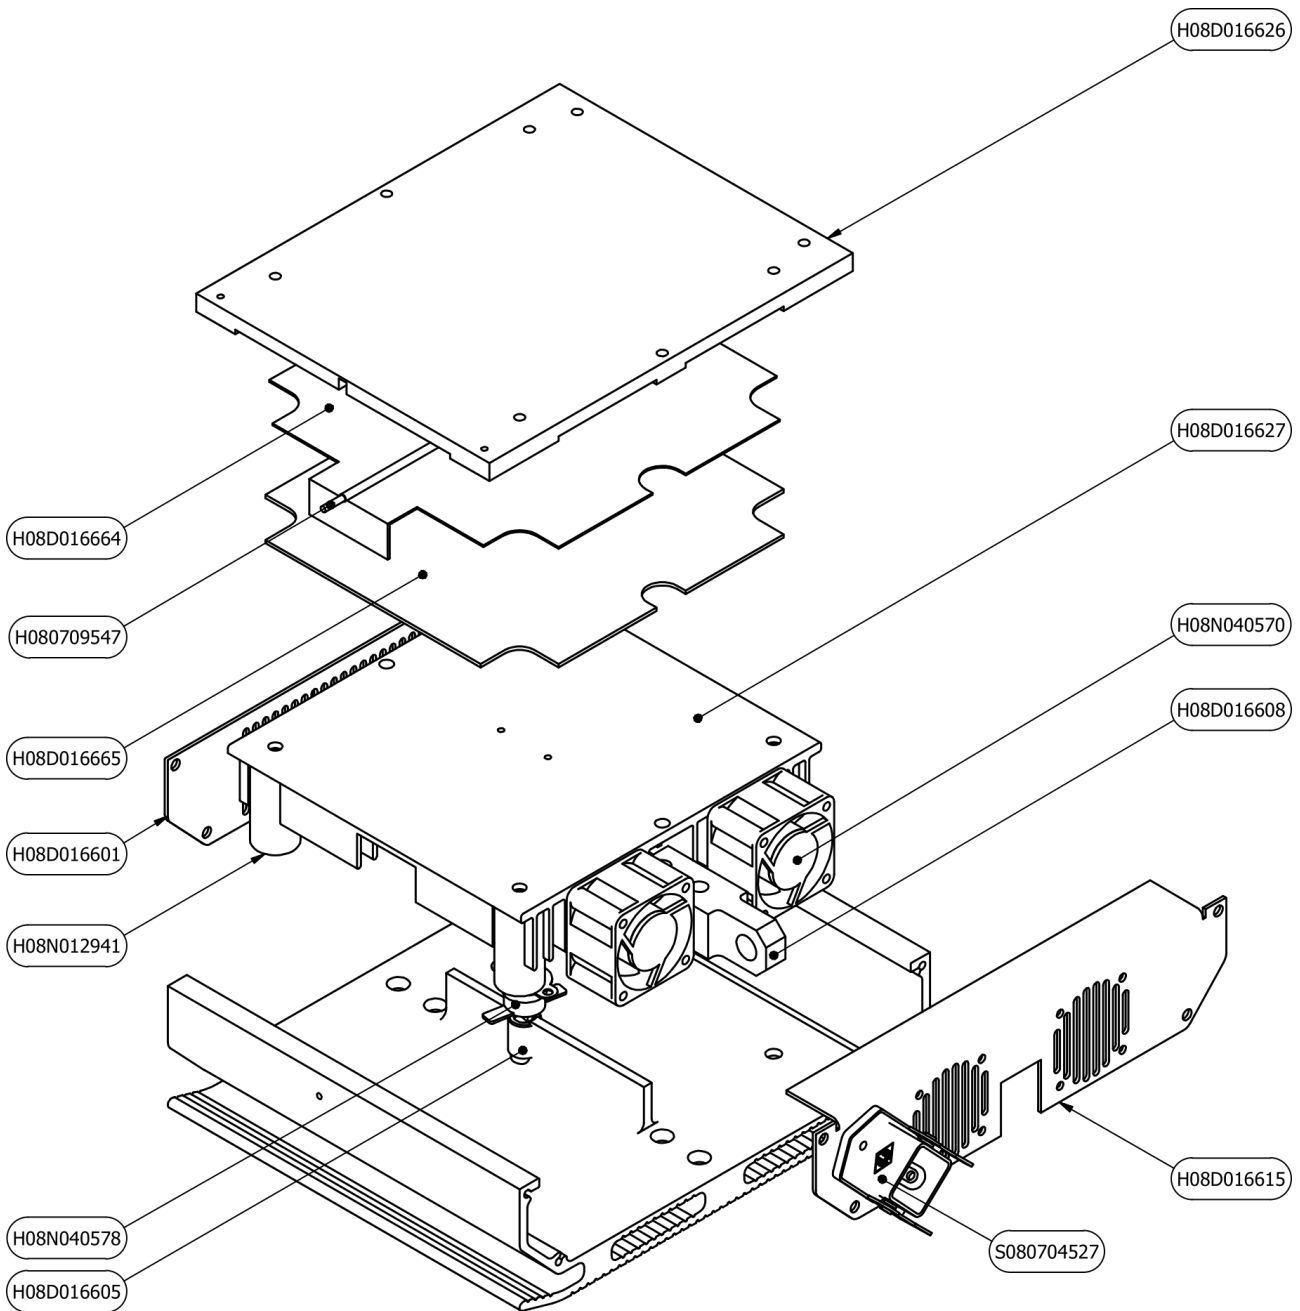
H08D016628 Untere Heizplattenbaugruppe PML-100
